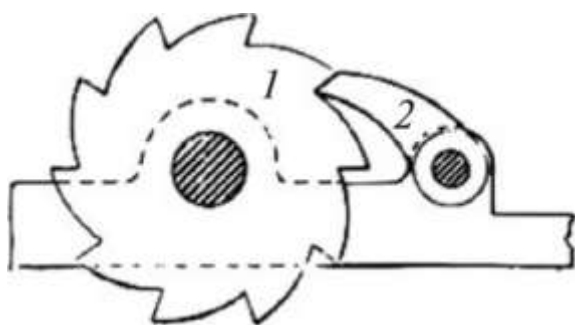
Храповой механизм: 1 — зубчатое колесо; 2 — собачка
